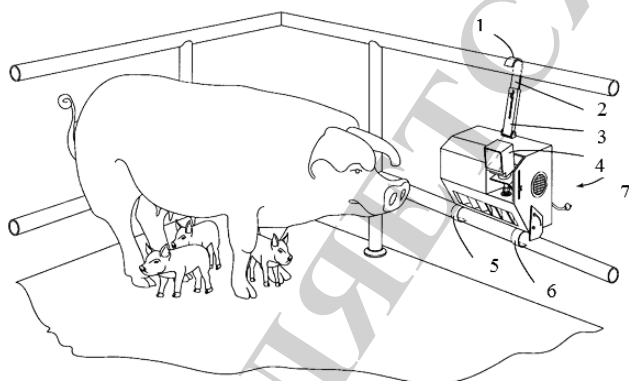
Пристрій для обігрівання поросят: 1 — с-подібний монтажний елемент; 2 — телескопічний елемент; 3 — кріпильний вузол; 4 — датчик руху; 5 — другий кріпильний елемент; 6 — с-подібний нижній монтажний елемент; 7 — опалювальний пристрій
